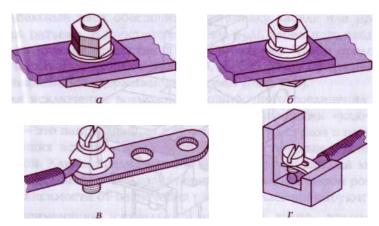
Болтовое соединение токопроводящих элементов: а — внахлест; б — внахлест с пружинистой шайбой; в — соединение провода с контакт-деталью; г — закрепление провода на плоской поверхности
